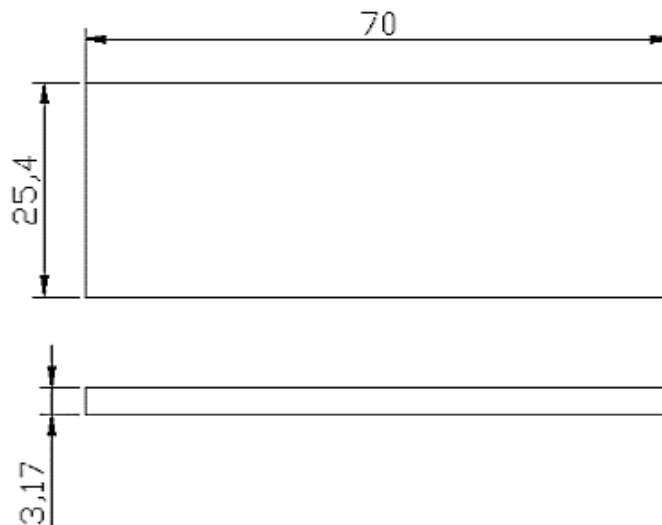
Dimensiones de la probeta a soldar. (Unidades en mm).
